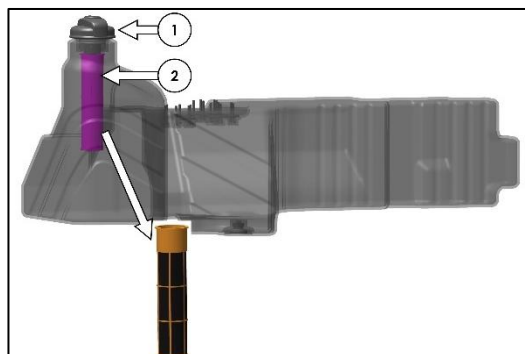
CRÉPINE DU RÉSERVOIR DE CARBURANT
